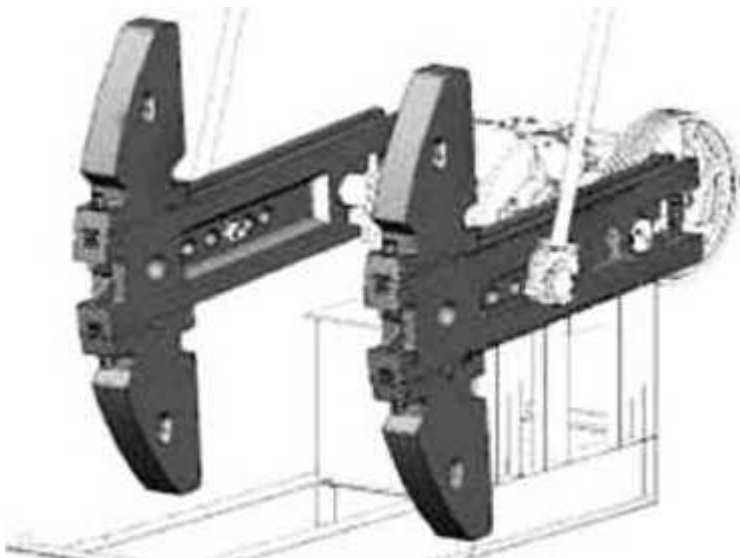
Кривошипно-шатунный механизм станка-качалки
